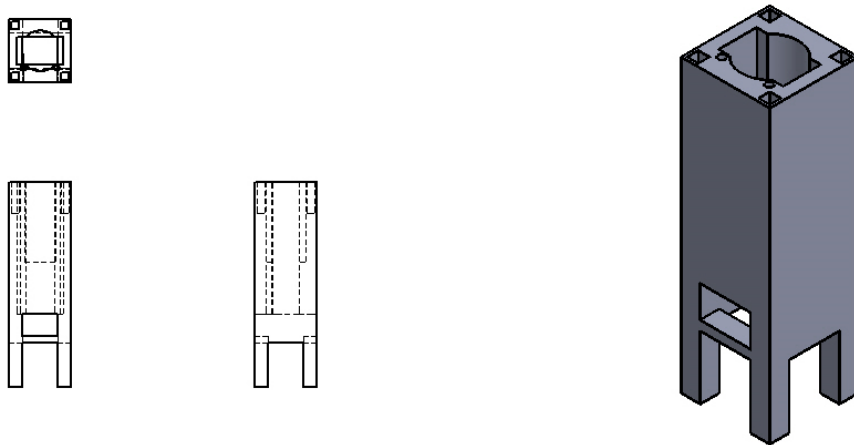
แบบวาด Bearing 3-6-2.5
